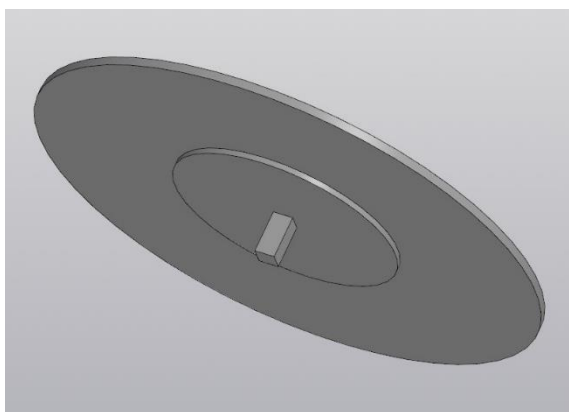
Опора для шагового двигателя и крепления для штатива
